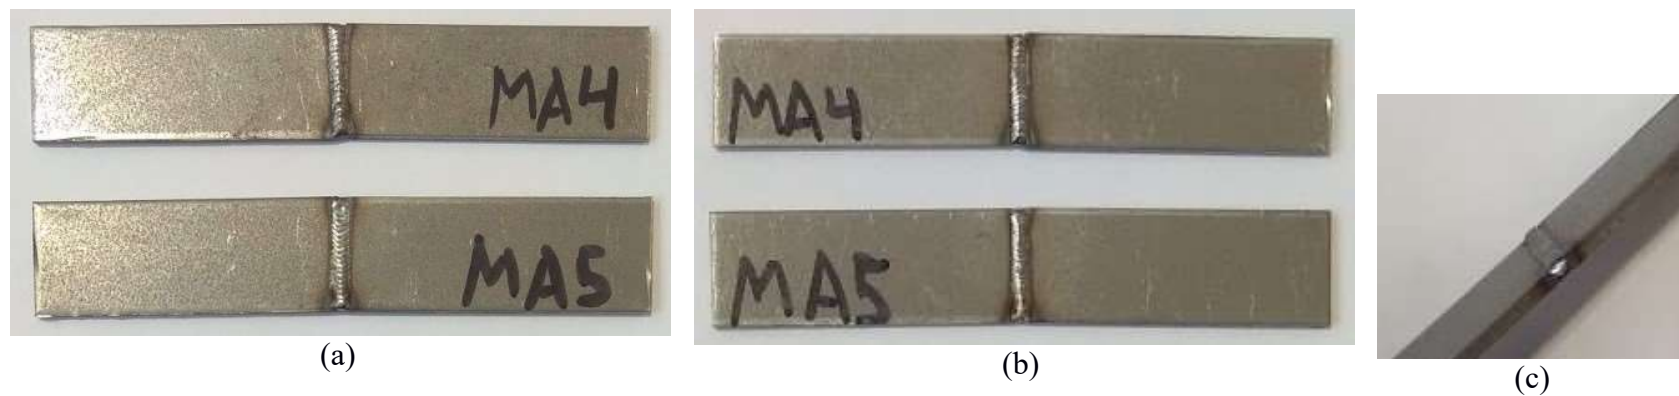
Amostras MA4 e MA5. (a) parte superior. (b) raiz da soldadura. (c) sobre espessura do cordão
